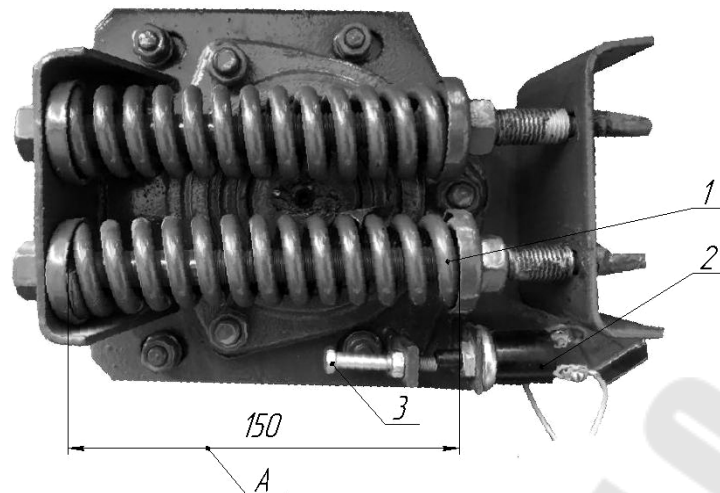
Механизм регулировки плотности прессования: 1 – пружина; 2 – датчик; 3 – головка болта
